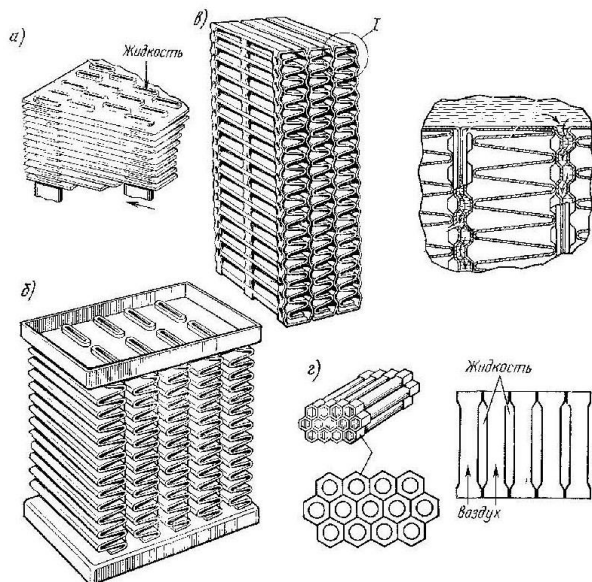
Решетки радиаторов трубчато-пластинчатого (а); трубчато-ленточного (б); пластинчатого (в); сотового (г)
